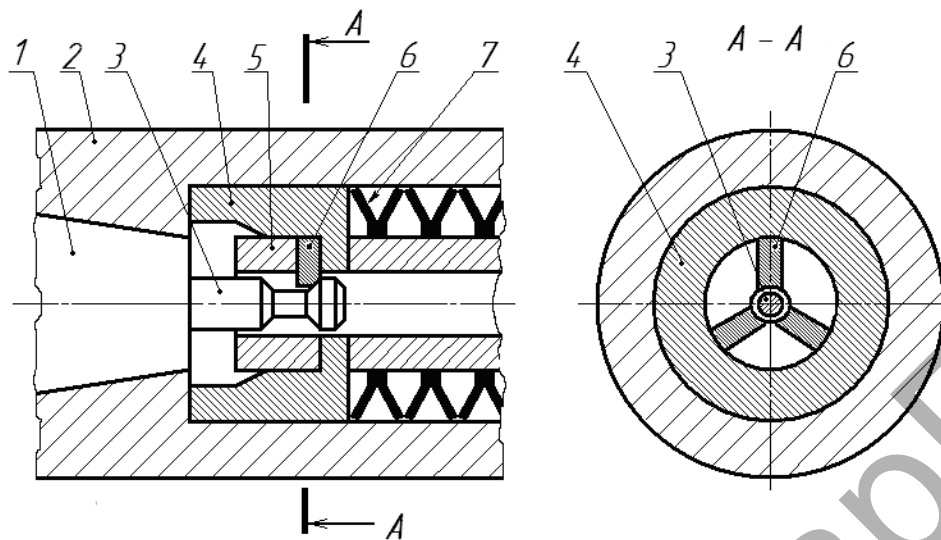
Схема зажима инструмента в шпинделе станка с помощью сухарей
